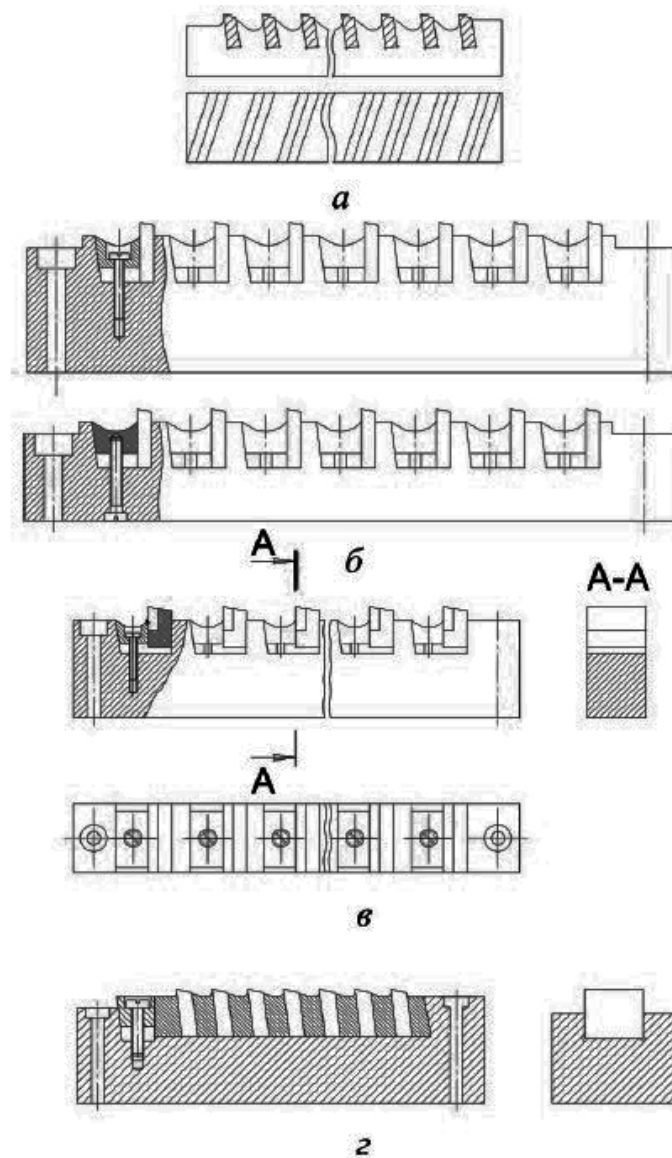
Нероз'ємне з'єднання зубців протяжки з корпусом (*a*);
